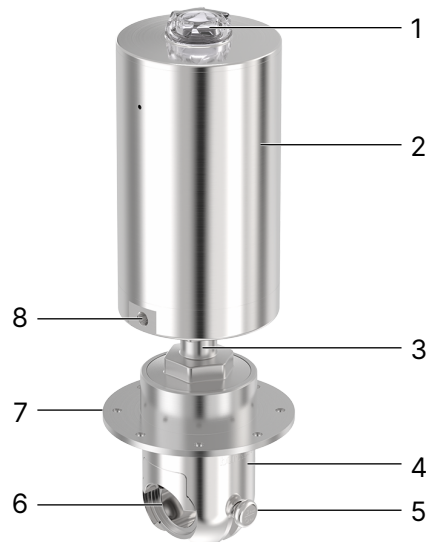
Aufbau des Schlauchquetschventils, INOX-Variante, Beispiel
